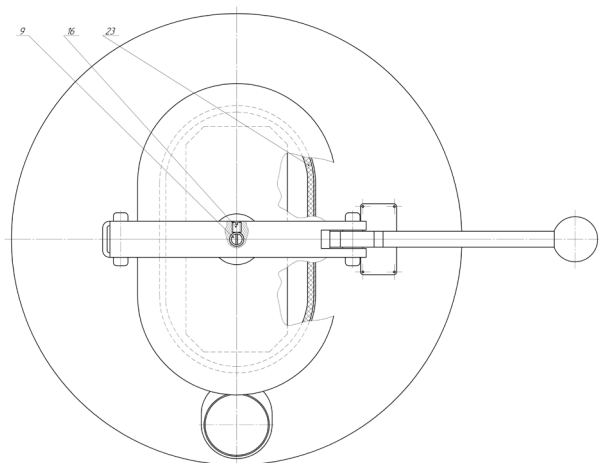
Общий вид устройства CARBOFit-400 (вид сверху)
